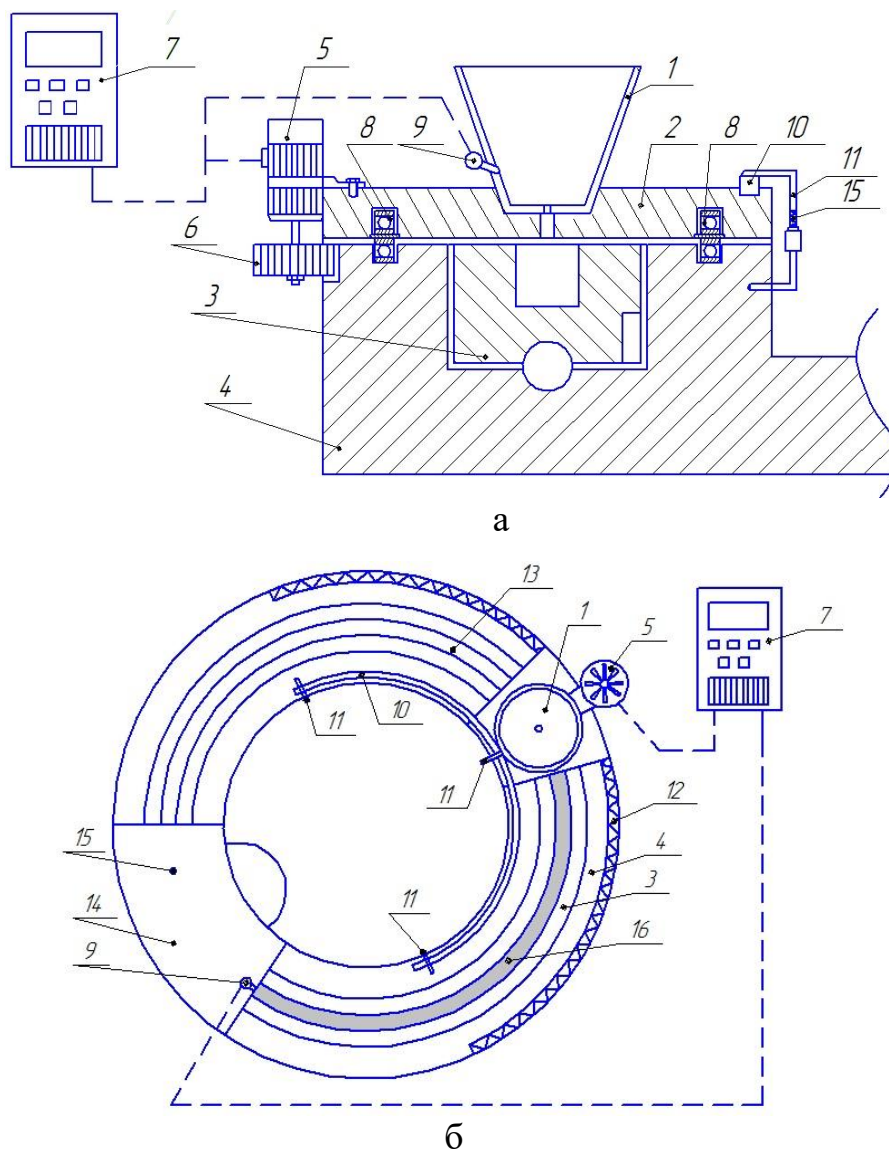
Схема устройства управления тепловым режимом установки НСЛиП с ГК:
